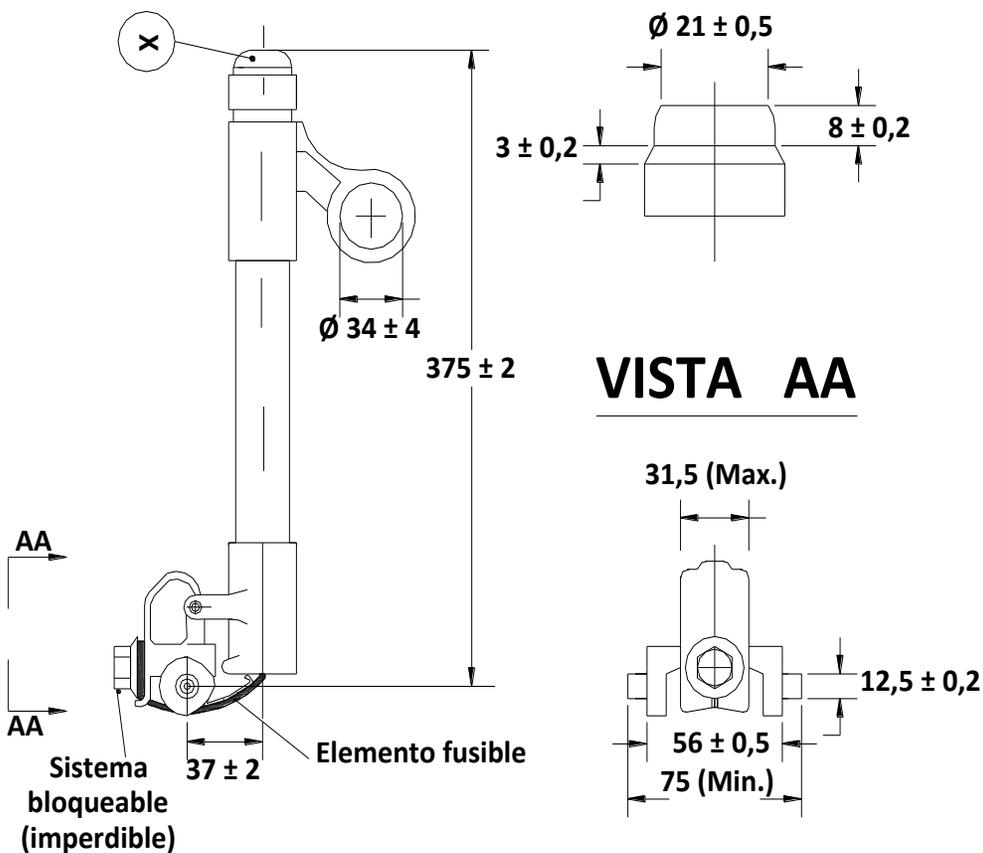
Tubo porta fusible para seccionador – Base Tipo C
